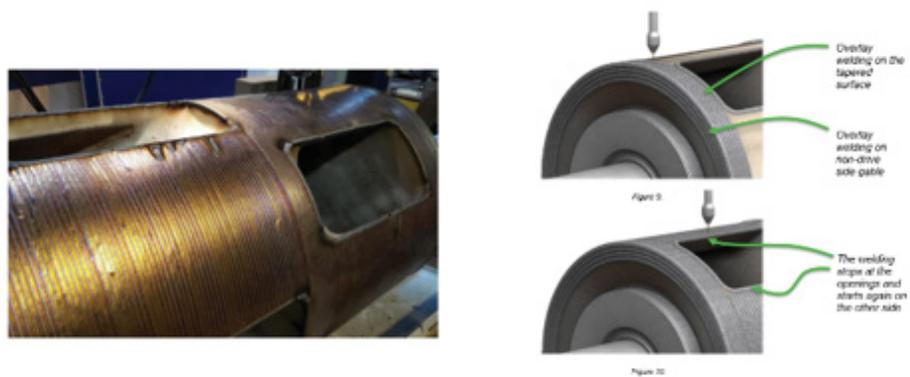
Rotor Durante Processo de Revestimento por Soldagem
